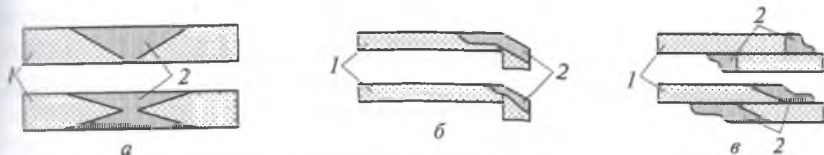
Схема сварки с использованием диспергированного расплава стыковых (а), угловых (б) и нахлесточных (в) соединений КМ:
